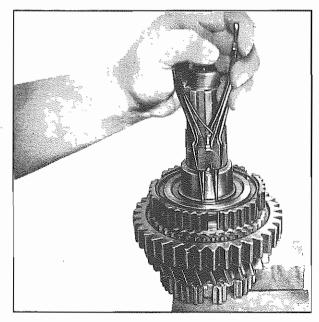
Togliere l'anello elastico di arresto Removing circlip
